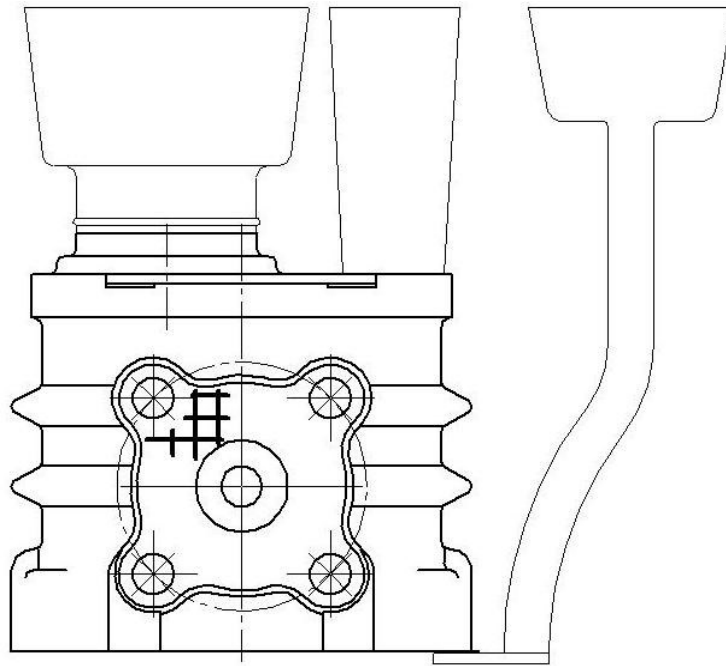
Конструкція ливникової системи виливка Корпус НШ100
